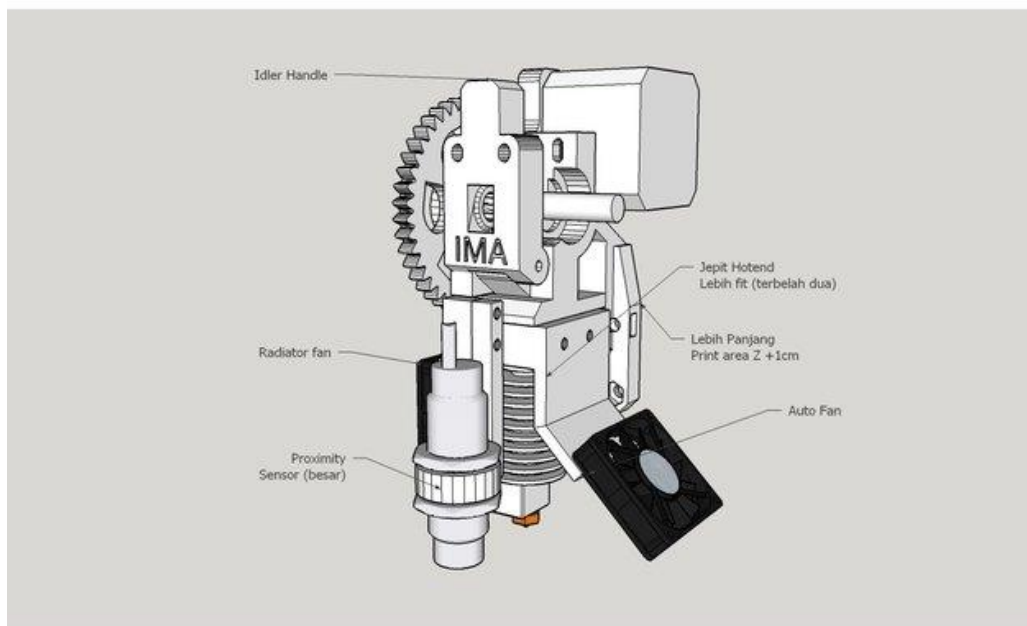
Extrusor engranado para final caliente E3D. (thingiverse, 2018)
